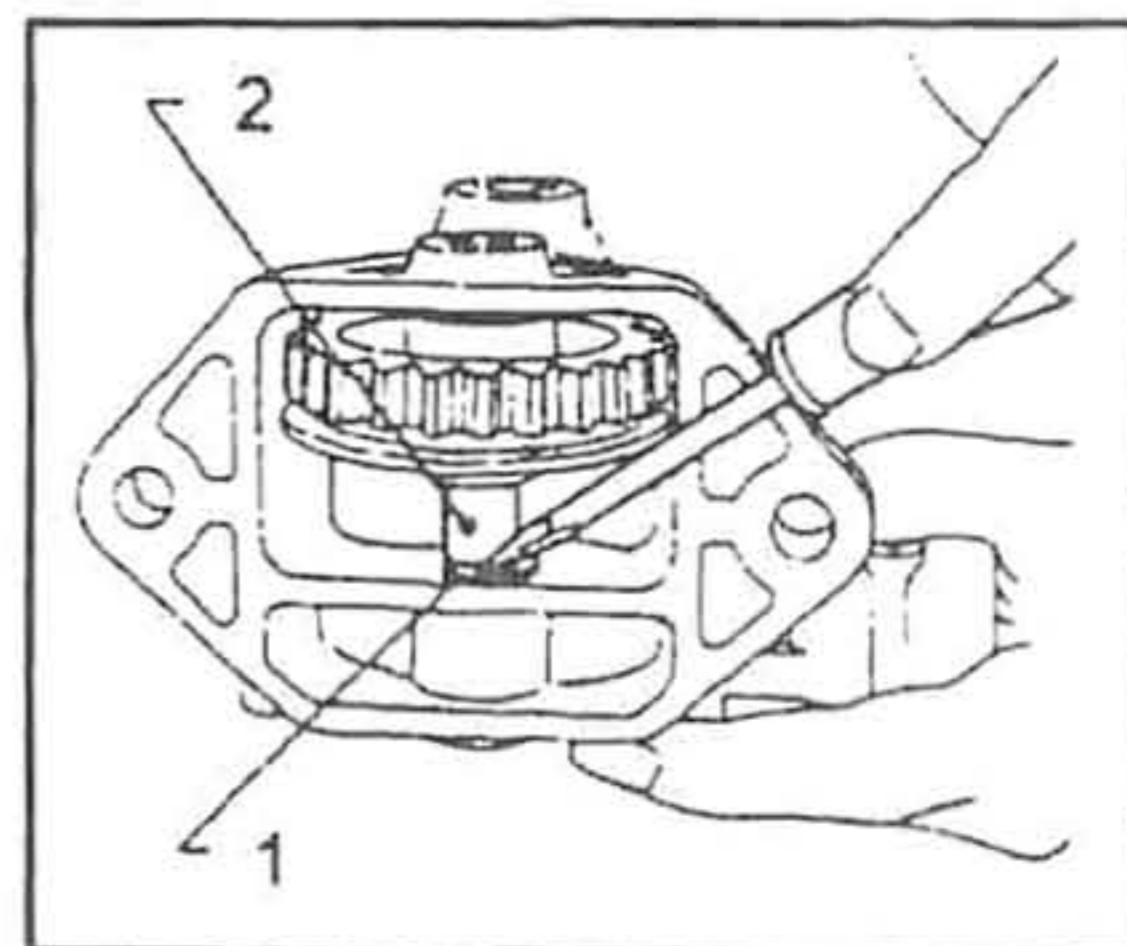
1. Пружинное упорное кольцо. 2. Вал промежуточной шестерни.
